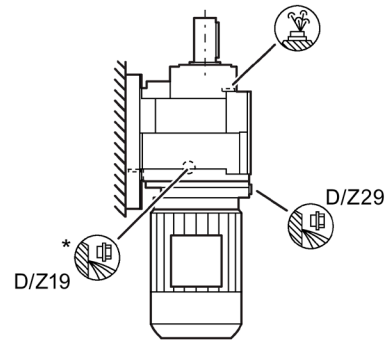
Einbaulagen für Stirnradgetriebe EF/EZ Flanschsausführung Baugrößen 39 - 149
